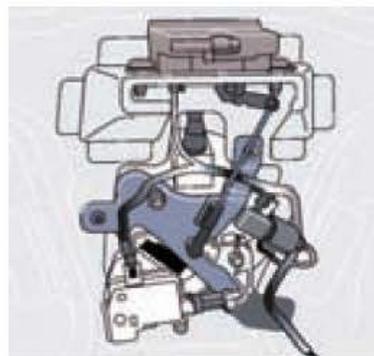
Conjunto de palancas y varillaje de una cerradura.
